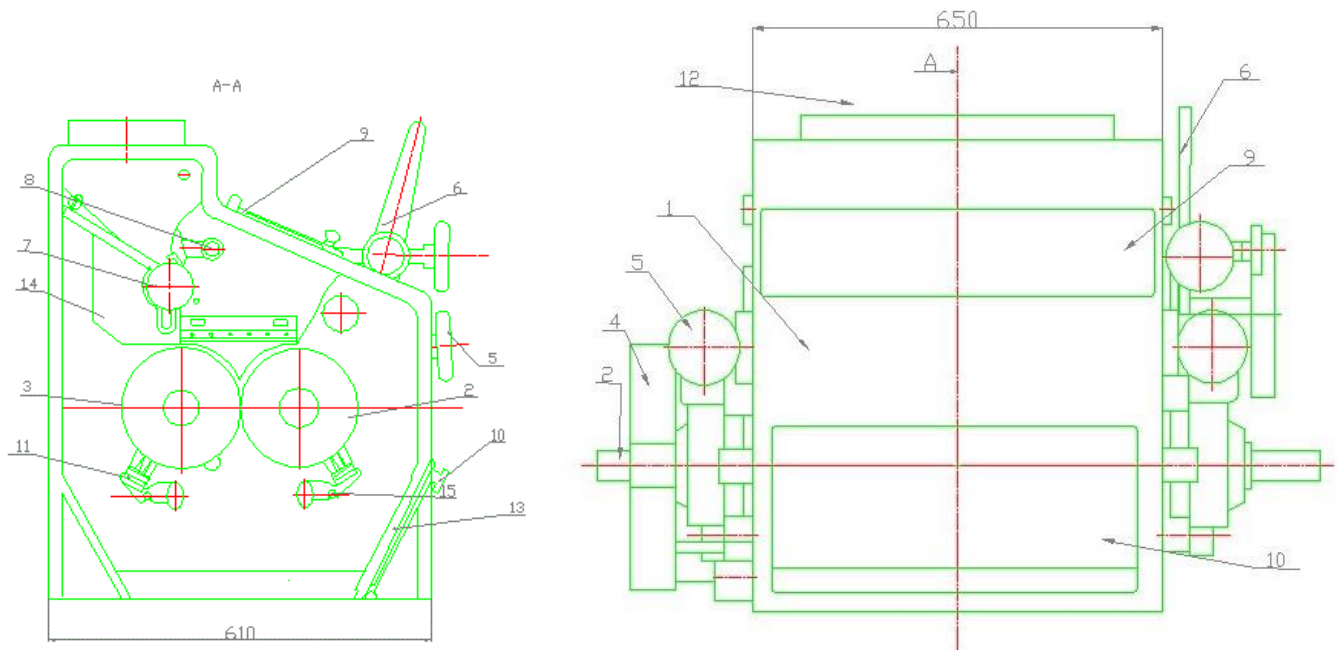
Вальцевий верстат марки P6-BC 185x250: 1- станина; 2- швидкий вал; 3- повільний вал; 4- міжвалкова передача; 5- механізм настроювання валків на паралельність; 6- привало-відкидний механізм; 7- живильний вал; 8- механізм регулювання живлення; 9- верхня дверка; 10- нижня дверка; 11- щітка; 12- живильна труба; 13- заслінка; 14- накладка; 15- вісь.
